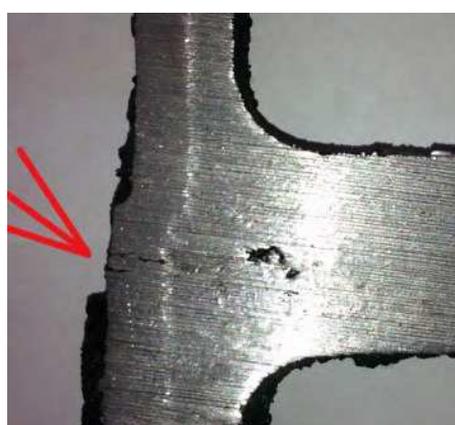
Фрагмент отливки с микротрещиной с наружной стороны отливки
